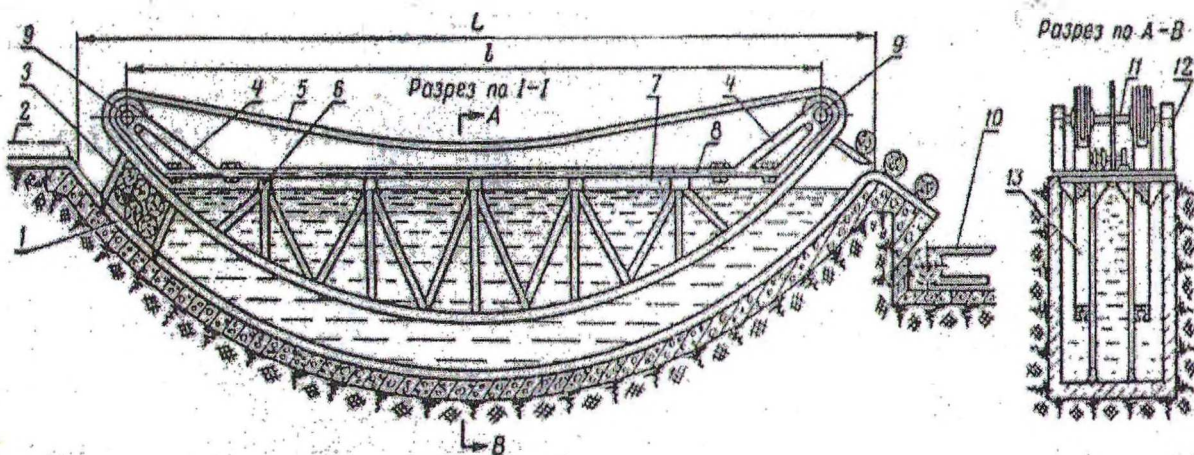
Цепной варочный бассейн: 1 – направляющие рельсы; 2, 3, 5, 10 – транспортеры; 4 – кронштейны; 6 – швеллер; 7 – каркас крыши; 8 – крышка; 9 – звездочки; 11 – валы; 12 – подшипники; 13 – направляющие цепей транспортера
